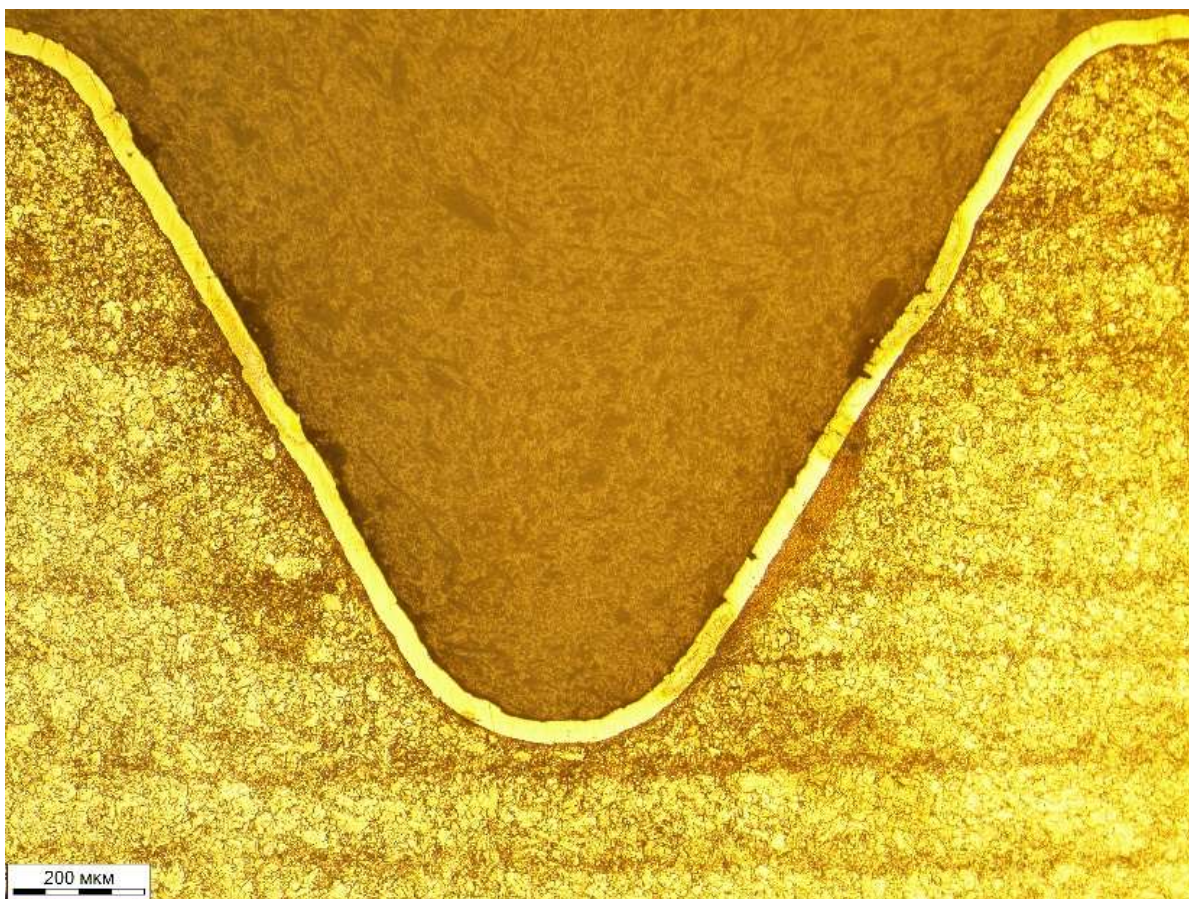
Вид участка резьбы шпильки с нанесенным защитным покрытием.
